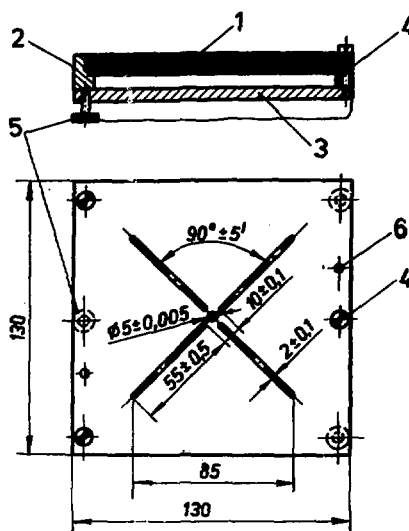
Реперный крест нижней рамы: 1 - конденсаторная люминесцентная пластина; 2 - корпус с вырезерезованными прорезями в виде креста; 3 - кронштейн; 4 - винт крепежный; 5 - винт юстировочный; 6 - штифт.
